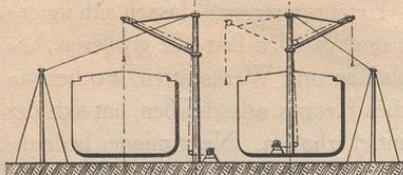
Helling mit versetzbaren hölzernen Mastenkranen.
